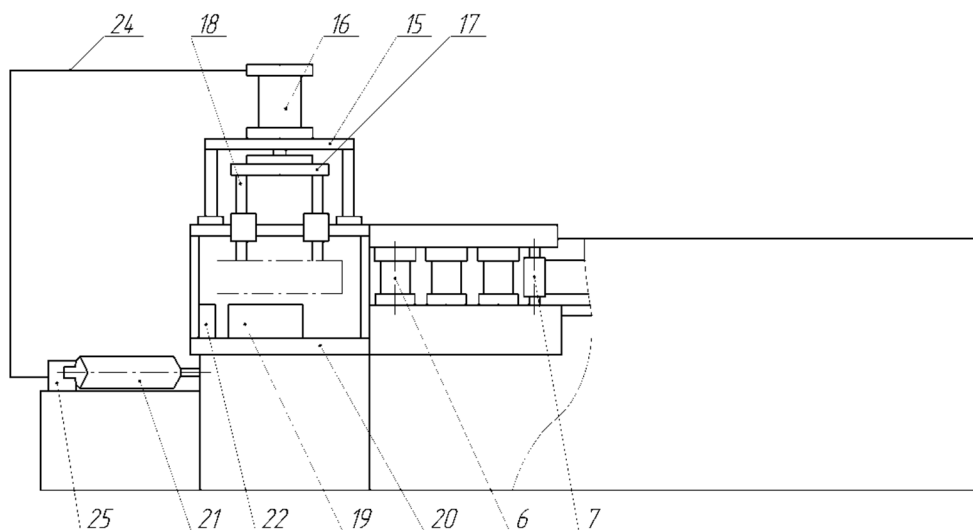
Принципиальная схема стана для прокатки заготовок малолистовых рессор автомобилей МАЗ (вид сбоку)
